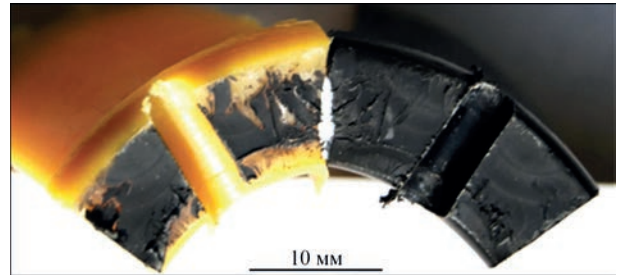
Поверхні руйнування зварного з'єднання труб з ПЕ80 діаметром 110 мм та товщиною стінки 10 мм
